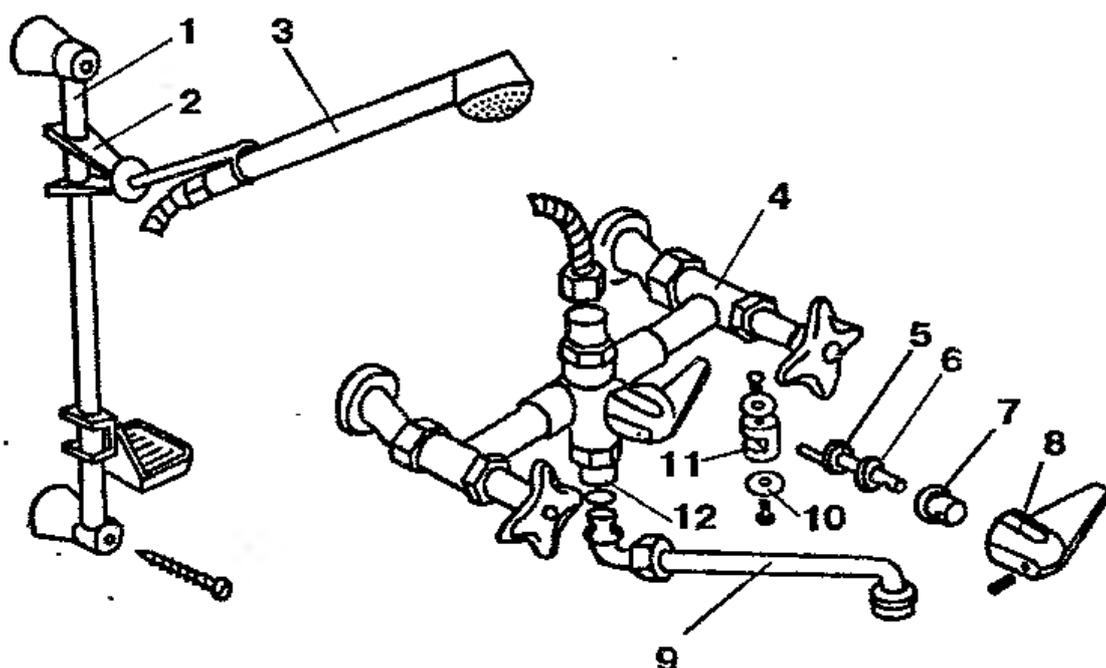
Смеситель с золотниковым переключателем, имеющим резиновые кольца и штангу: 1 — штанга; 2 — держатель; 3 — душевая сетка; 4 — корпус; 5 — кривошип; 6 — нитяное уплотнение; 7 — специальный винт; 8 — рукоятка; 9 — излив; 10 — прокладка золотника; 11 — золотник; 12 — переходник
